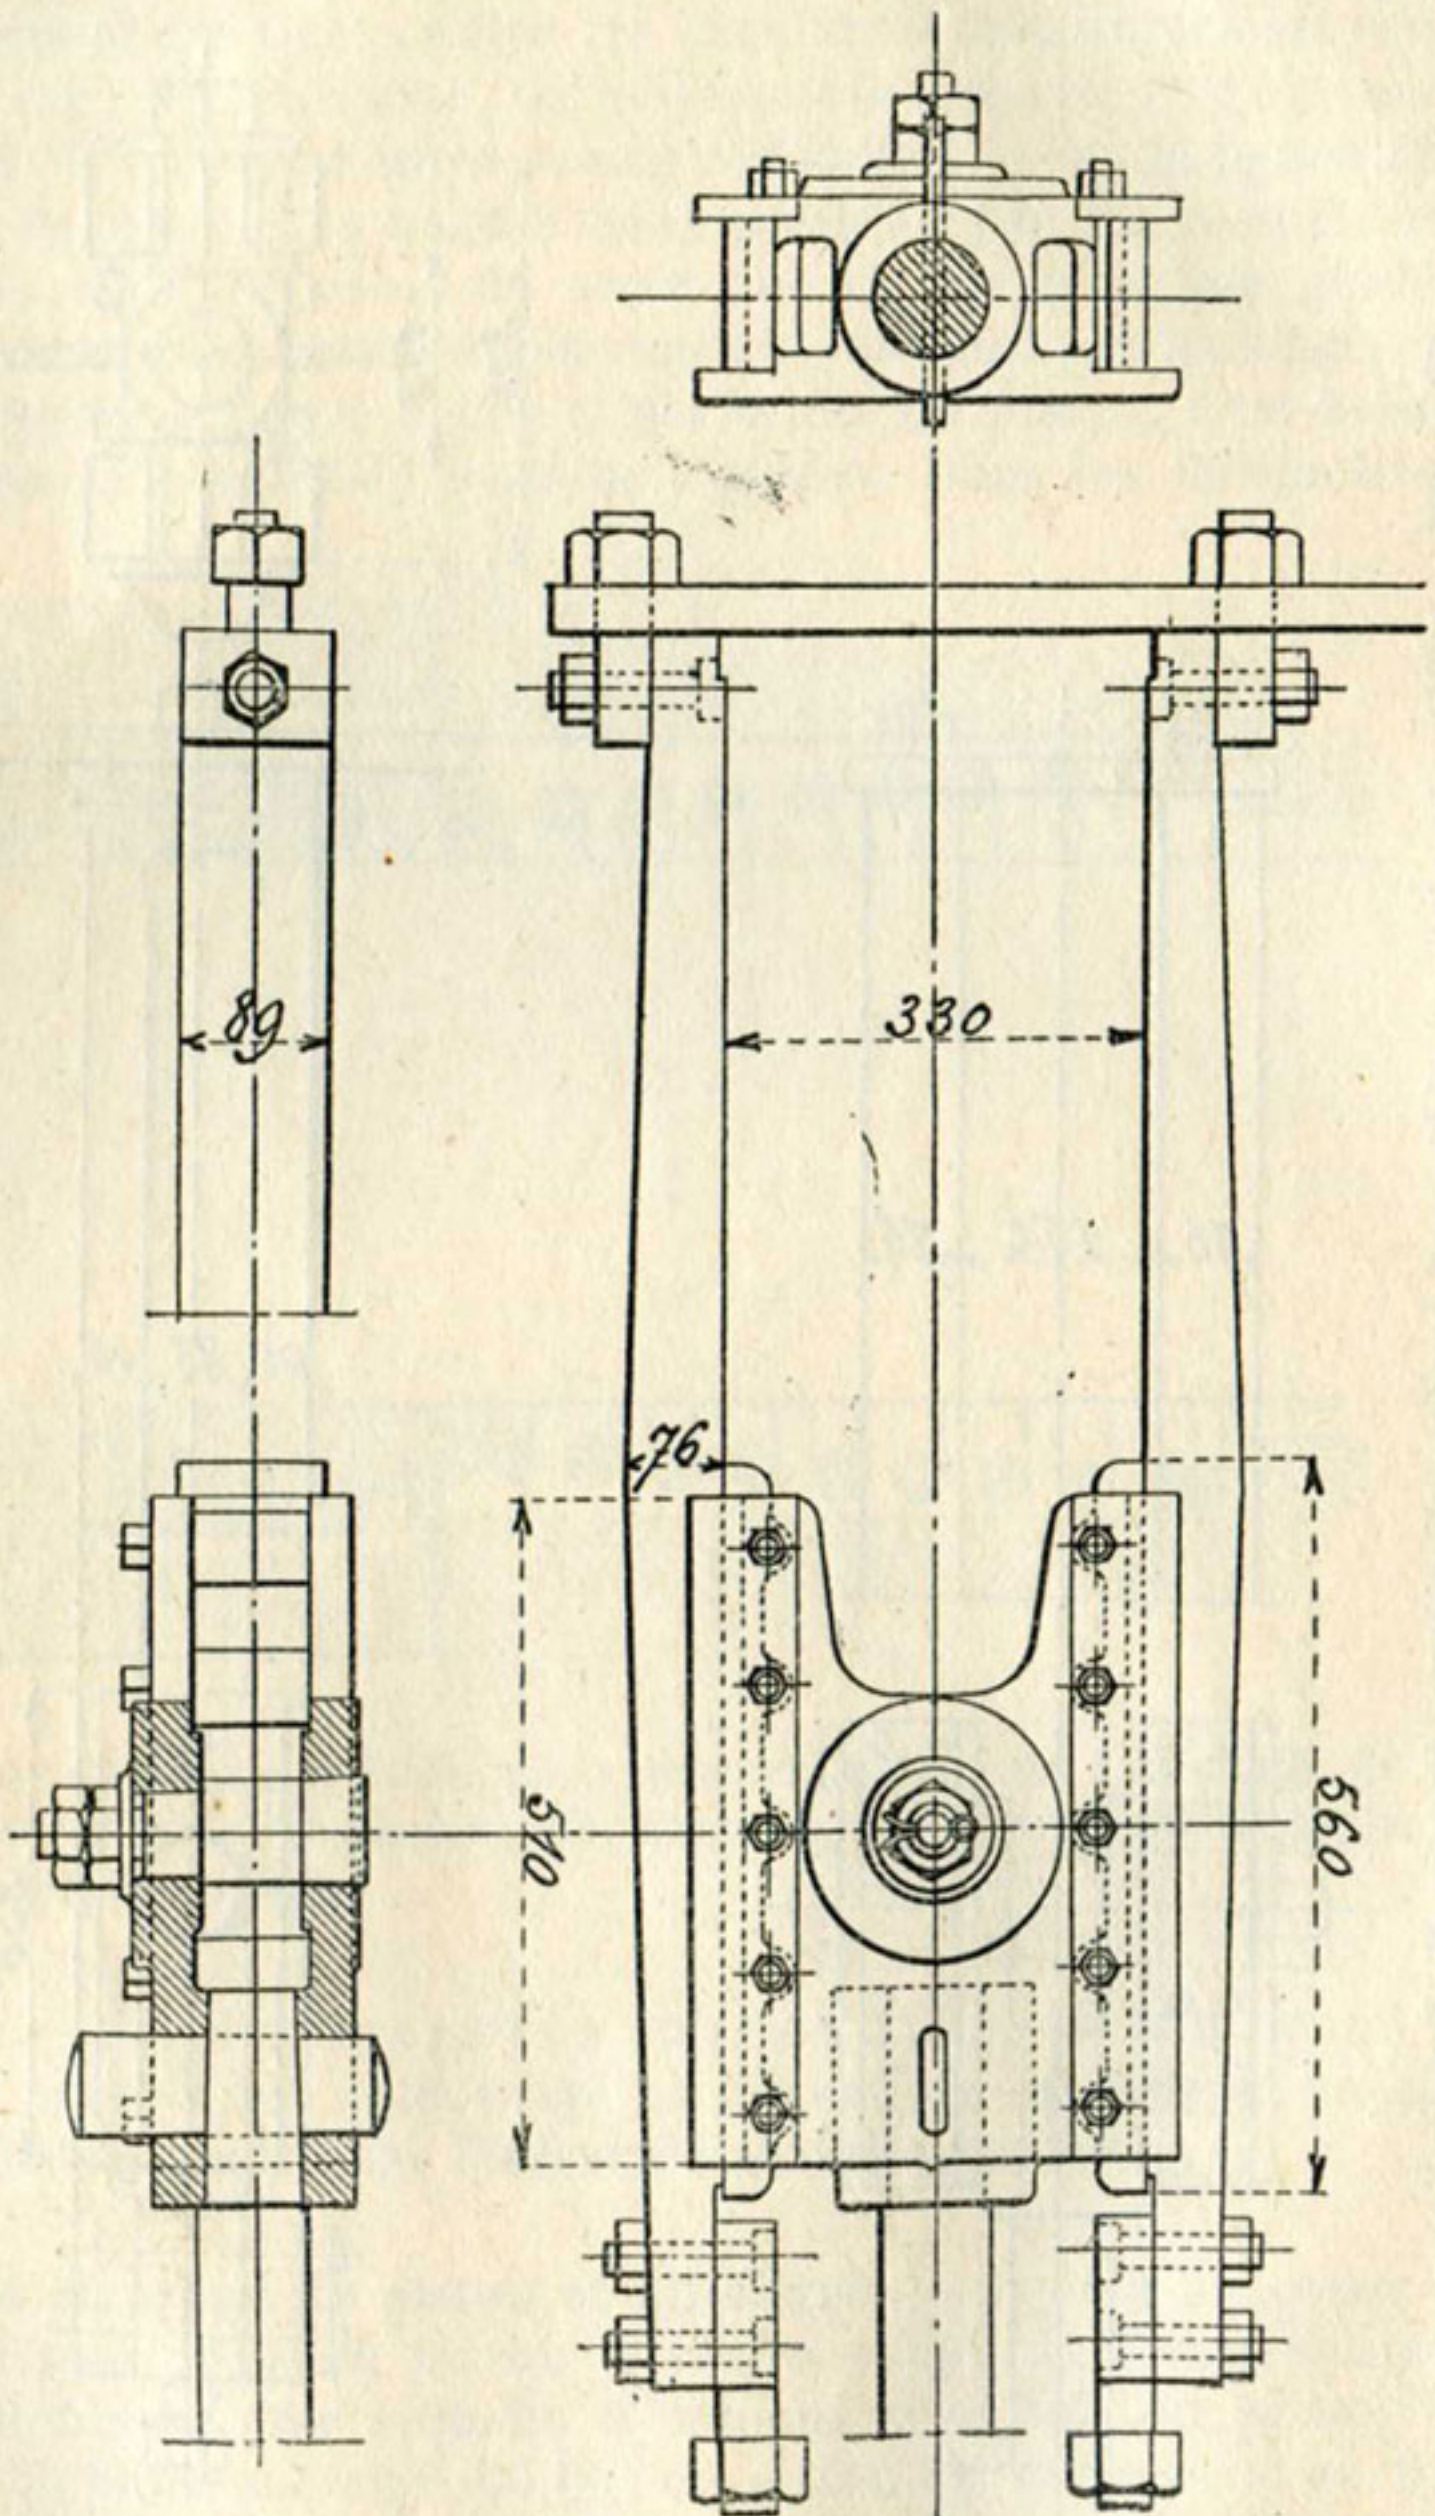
Tête de piston guidée par deux glissières (d'après M. Demoulin).
